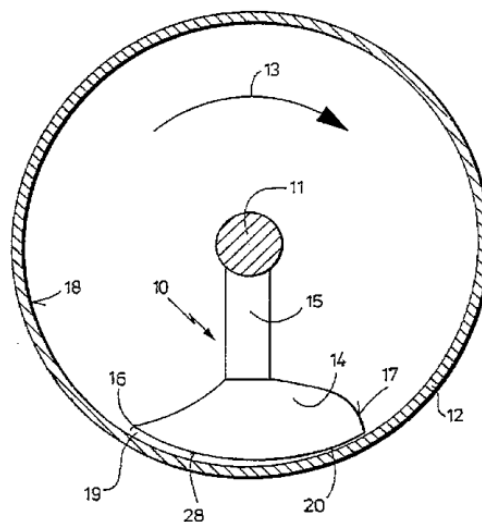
Ansicht modifiziertes Mischwerkzeug im Querschnitt [6]
